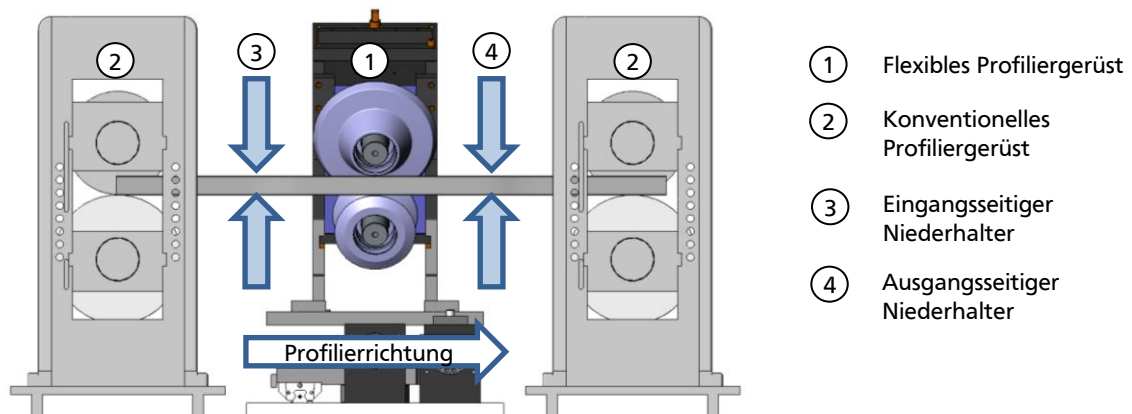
Werkzeugsystem mit flexiblem Walzprofiliergerüst, konventionellen Antriebsgerüsten und schematischer Darstellung von Niederhaltern vor und hinter dem flexiblen Profiliergerüst
